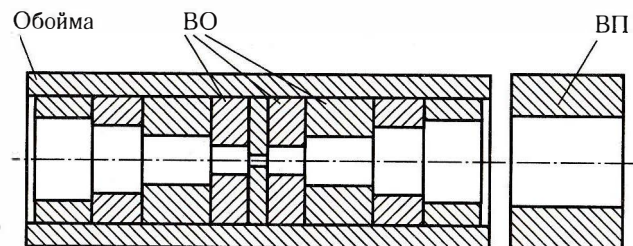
Ступенчатый конический коллиматор: ВО – втулки конического отверстия; ВП – втулка перекрытия зазора
